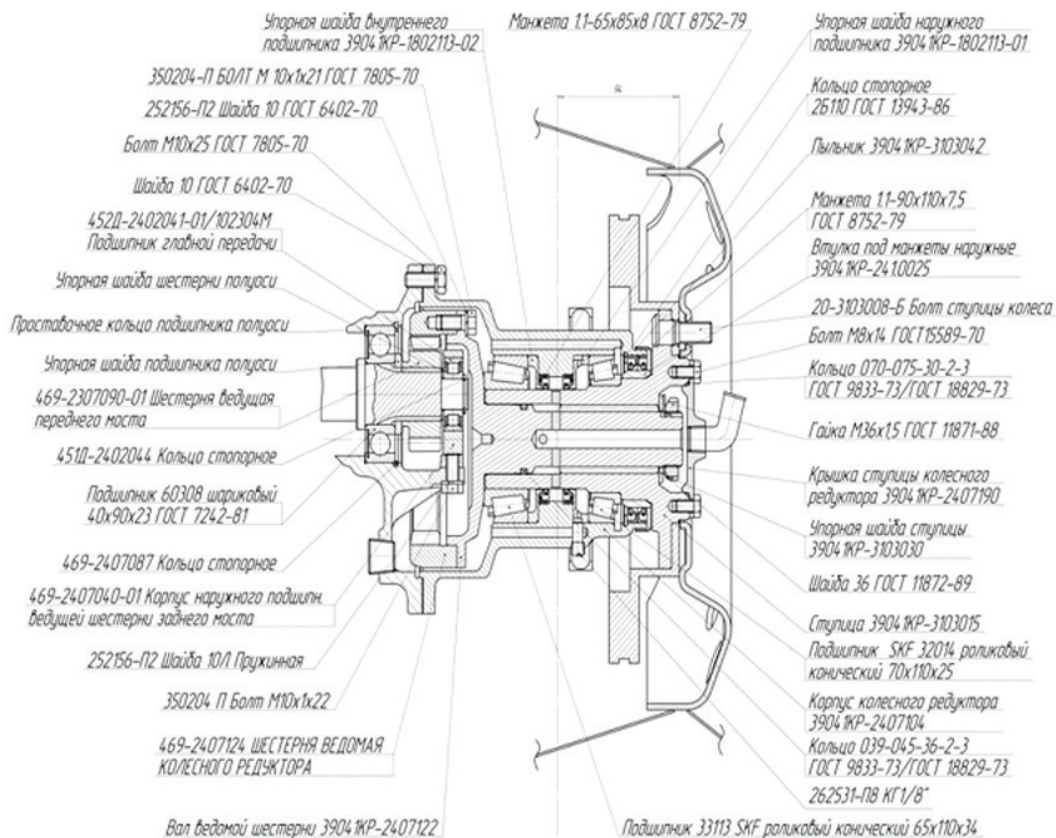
колёсный редуктор ТРЭКОЛ-3904КР
